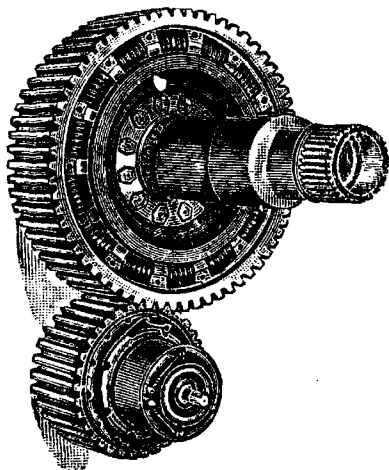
Планетарный редуктор двигателя Рольс-Ройс 300 НР.
